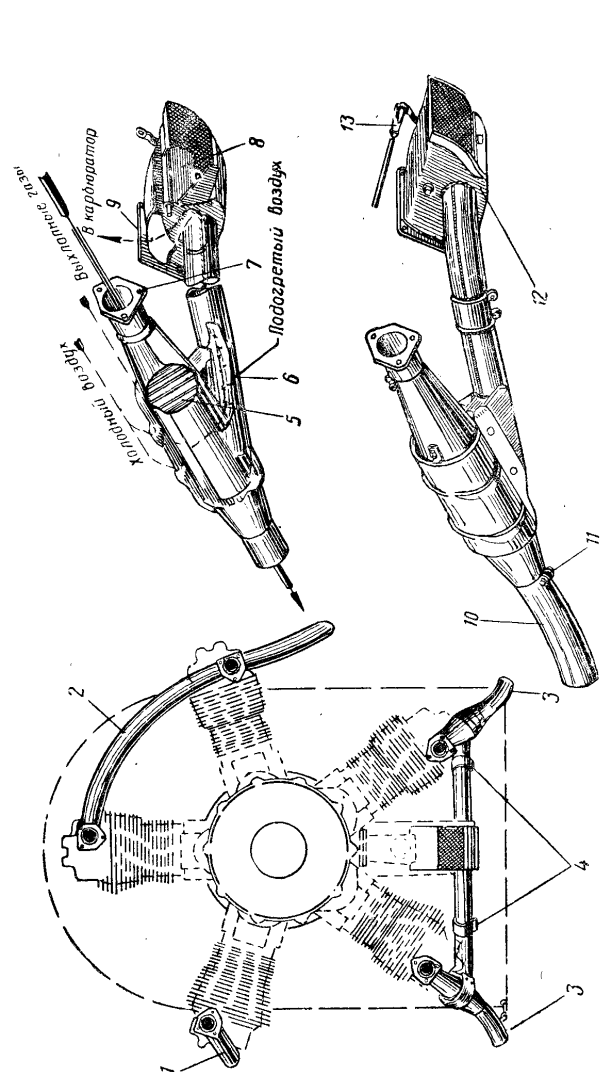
Установка выхлопных патрубков и подогревателя воздуха.
